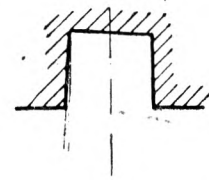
Сечение паза с непараллельными стенками, изготовленного при фрезеровании с маятниковой подачей
